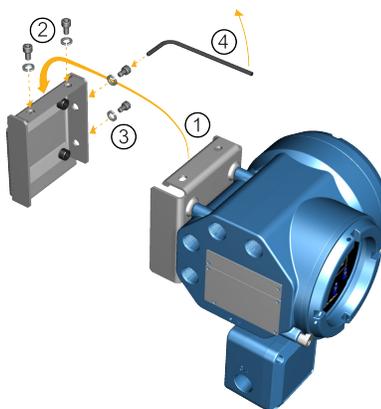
Кронштейн для настенного монтажа и размеры для преобразователя в корпусе из нержавеющей стали
